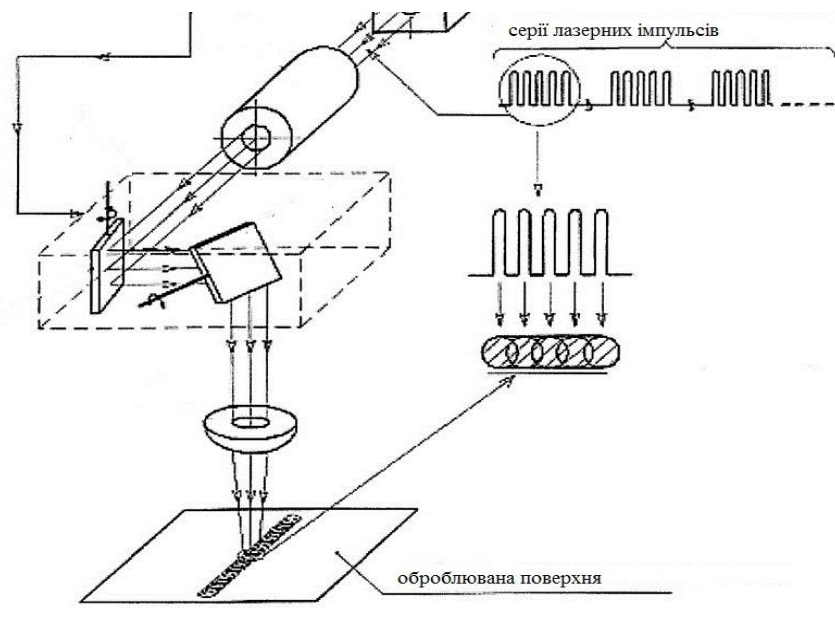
Спосіб поверхневої лазерної обробки
